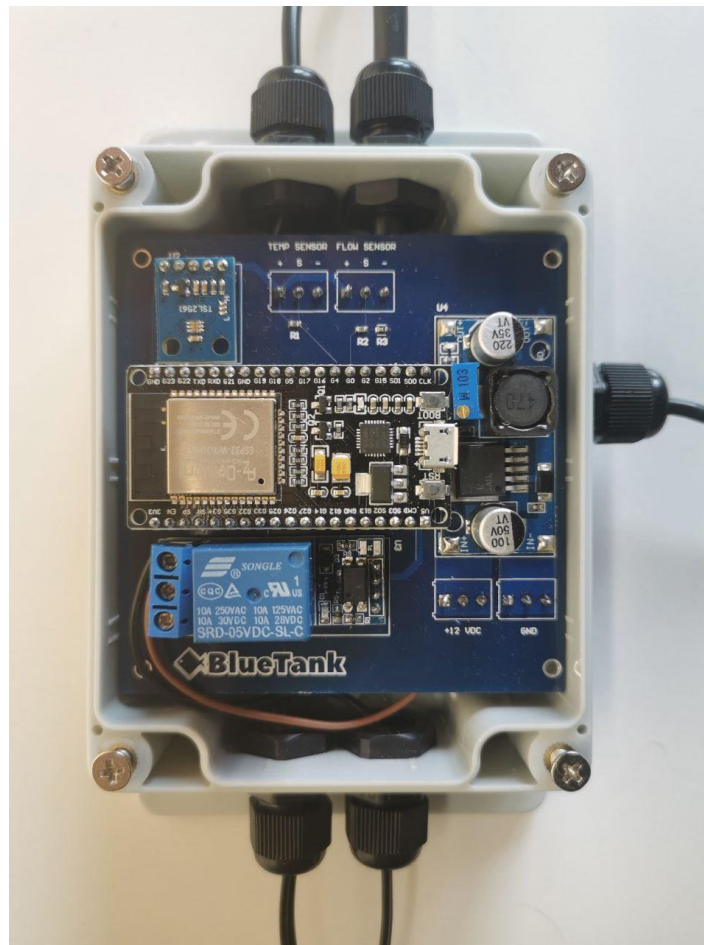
Placa soldada y montada en la caja con conectores prensaestopas
